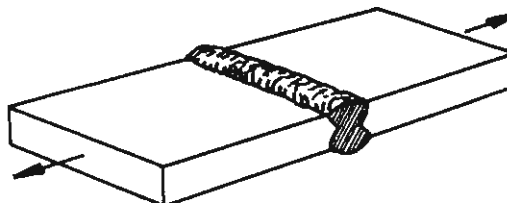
Fissuration par fatigue d'une soudure bout à bout transversale.
